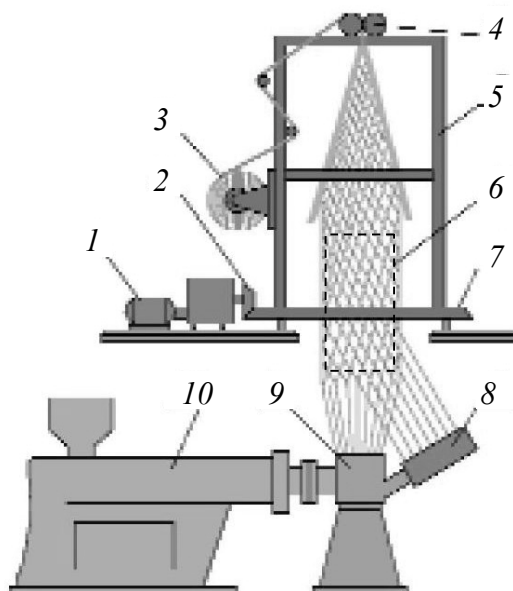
Способ получения рукавных полимерных сеток из экструдированных стренг с их термосваркой на вращающейся оправке: 1 – электродвигатель; 2 – шестерня; 3 – рулон готовой сетки; 4 – тянущие валки; 5 – рама; 6 – оправка; 7 – зубчатое колесо; 8, 9 – кольцевой и щелевой мундштуки, соответственно; 10 – экструдер
